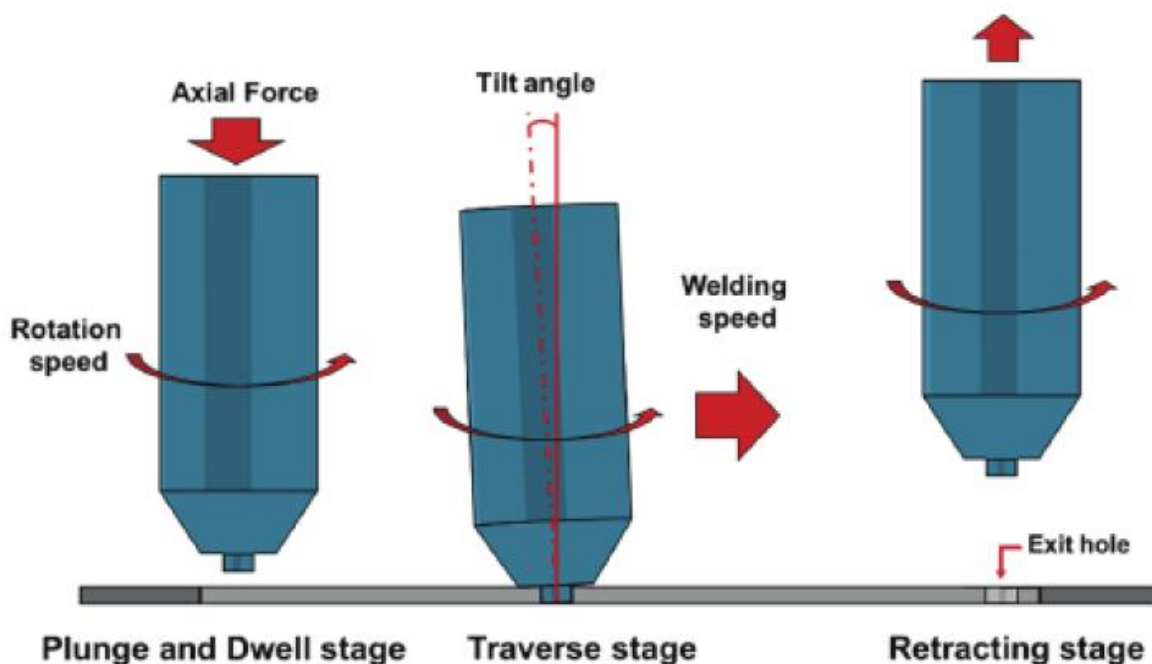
Схема процесса сварки трением с перемешиванием, включая различные стадии сварки и основные параметры сварки [118]
